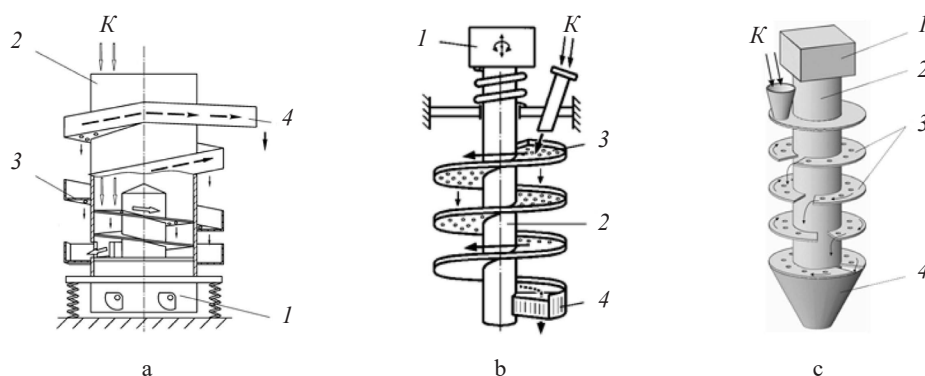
Конструкции вертикальных вибрационных смесителей: а – подъемный смеситель; б – проточный смеситель; в – каскадный смеситель (1 – вибропривод; 2 – цилиндрическая несущая колонна; 3 – перфорированный рабочий орган; 4 – выгрузочный патрубок; К – компоненты; стрелками показаны материальные потоки)
